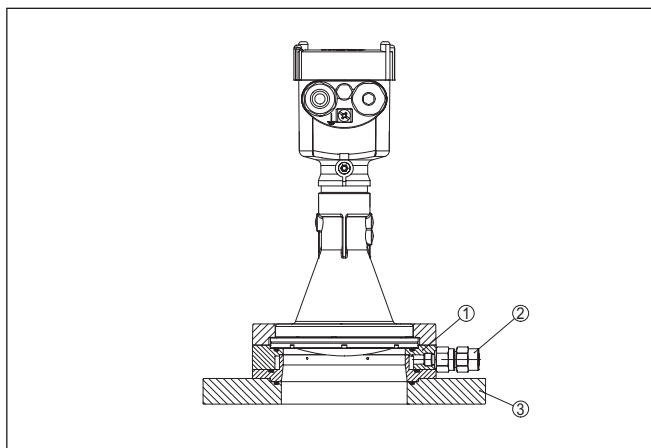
Продувочное присоединение для радарного датчика с адаптерным фланцем
